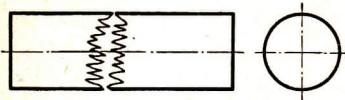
Bruchlinie bei Werkstücken aus Holz beliebigen Querschnitts
